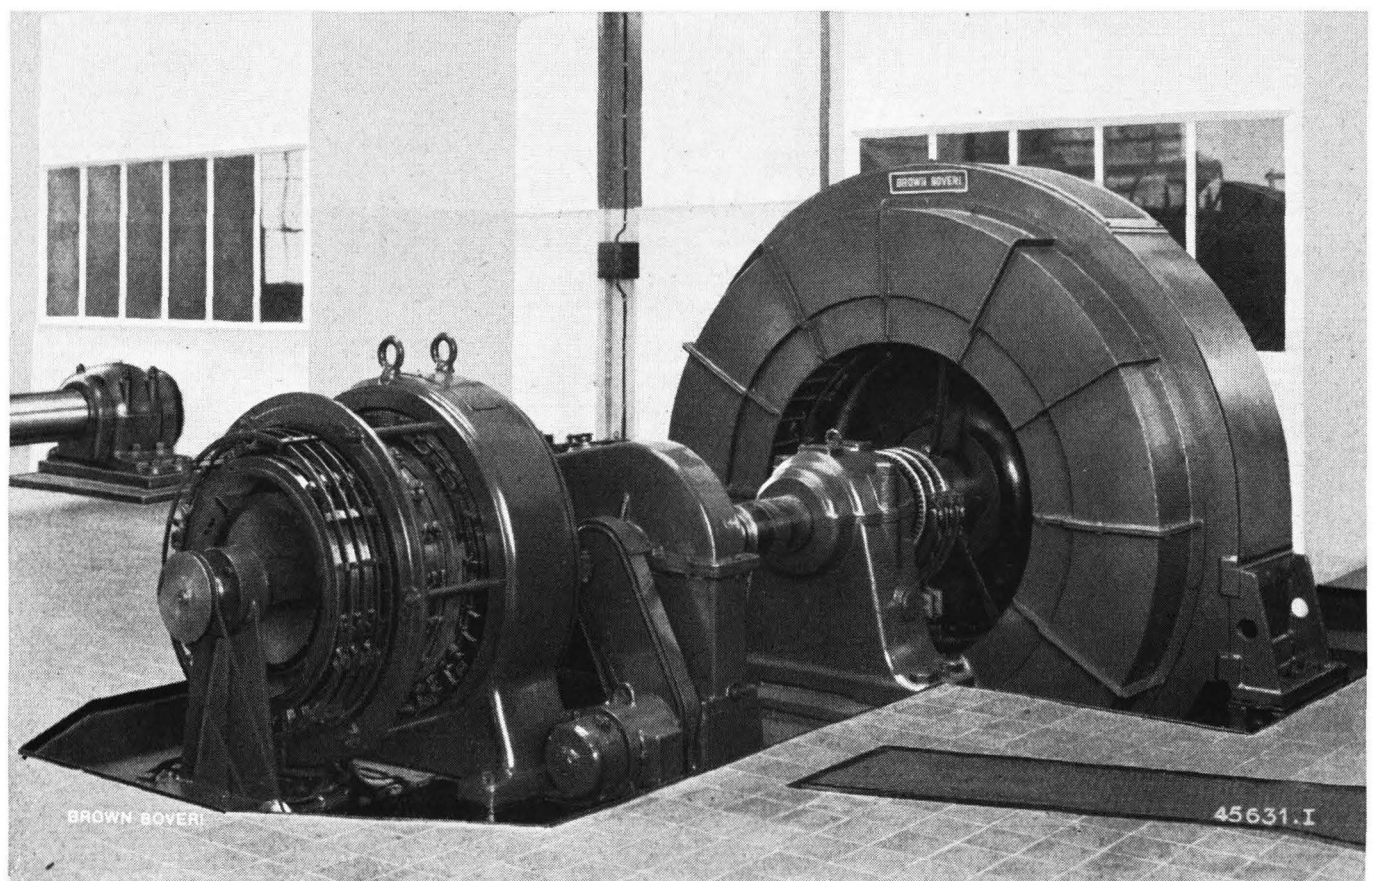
Dreiphasen-Walzwerkmotor, 960 kW, 330 U/min, 6000 V, 50 Per/s, mit Frequenzumformer.
